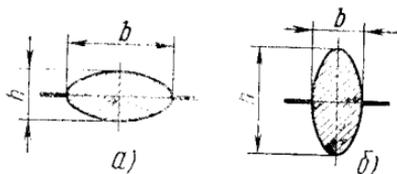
Типовое сечение поковки высотой h и шириной b , которое заполняется:
